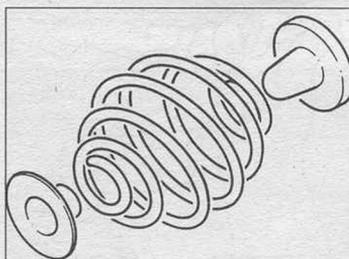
Задняя цилиндрическая пружина и резиновый демпфер (Глава 14)
